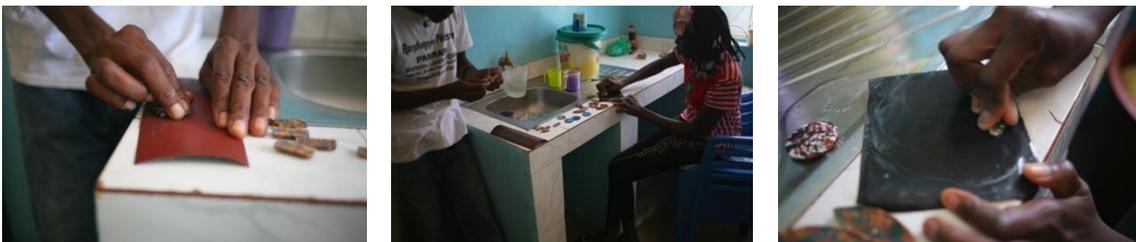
LIJADO DE PIEZAS EN EL TALLER. FUENTE: PROPIA
